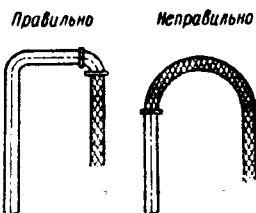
Схема подсоединения шланга к жесткому трубопроводу.
